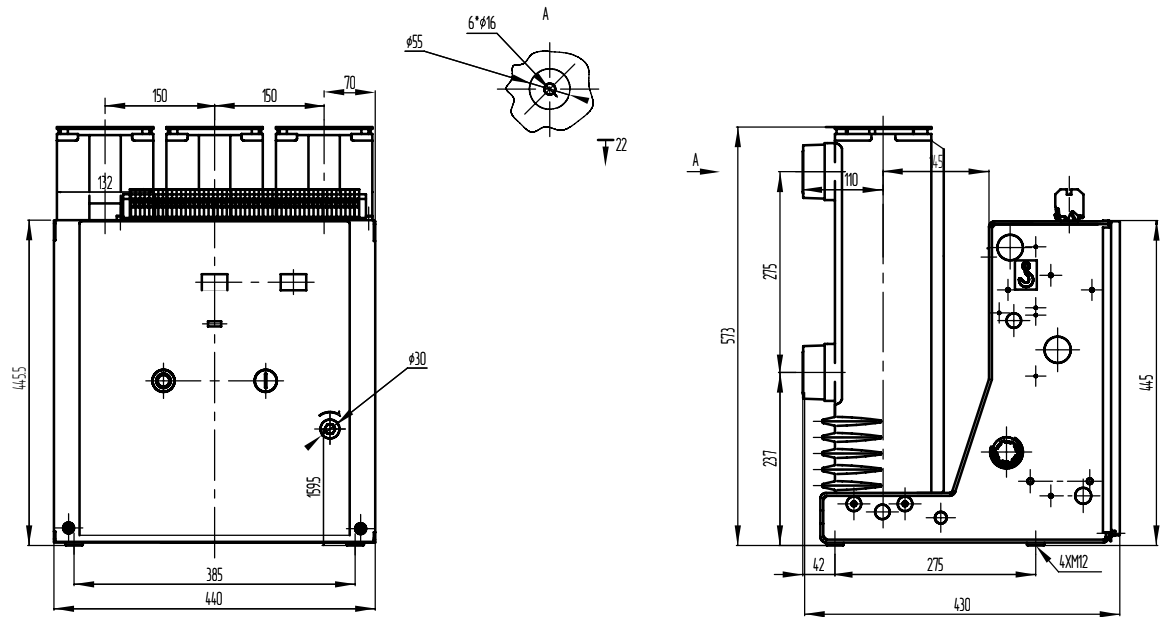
Габаритный размер выключателя ВВ-12 стационарного исполнения для ячейки шириной 800 мм
